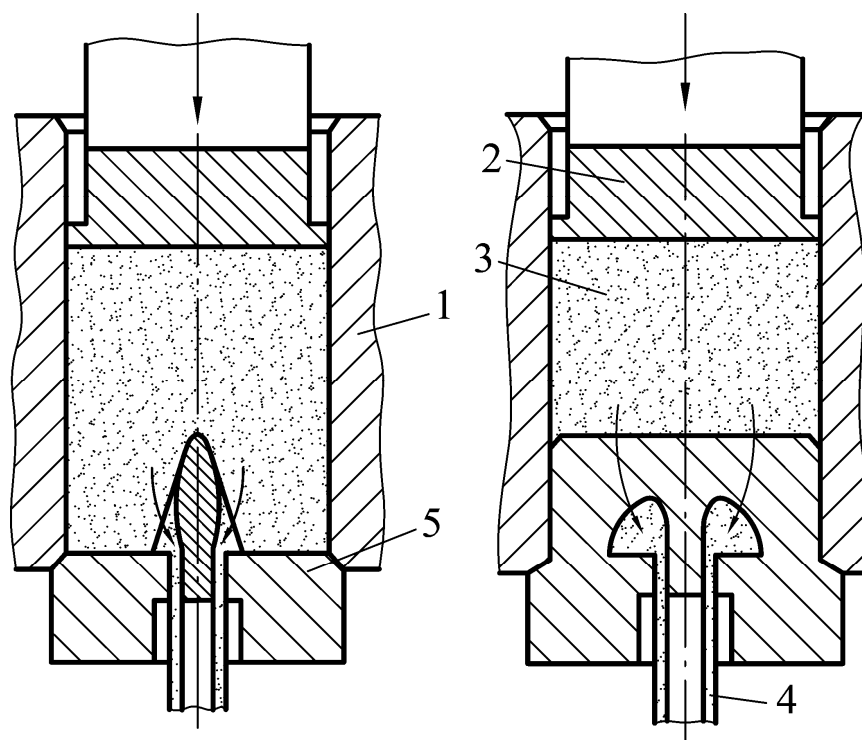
Схема прессования через комбинированную матрицу: 1 – контейнер; 2 – пресс-шайба; 3 – заготовка; 4 – полый профиль; 5 – матрица
